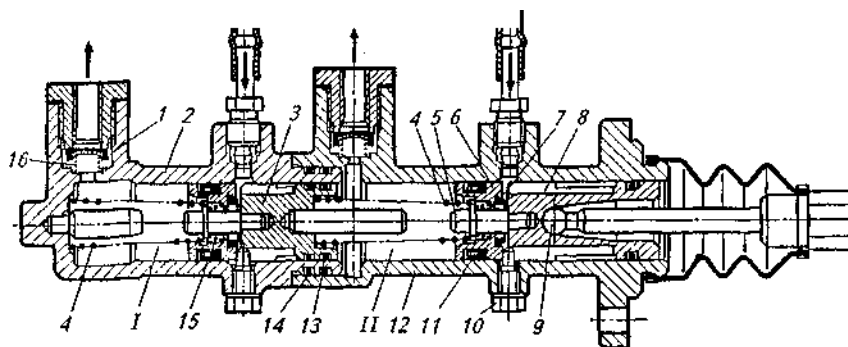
Главный тормозной цилиндр автомобилей ГАЗ: I, II — полости главного тормозного цилиндра; 1 — клапан избыточного давления; 2, 12 — соответственно вторичный и первичный картеры; 3, 8 — соответственно вторичный и первичный поршни; 4 — возвратные пружины поршня; 5 — упорный стержень; 6 — головка поршня; 7 — уплотнительное торцевое кольцо; 9 — толкатель; 10 — упорный болт; 11 — манжета; 13, 14 — соответственно уплотнительные кольца поршня и корпуса; 15 — пружина головки поршня; 16 — пружина клапана избыточного давления
